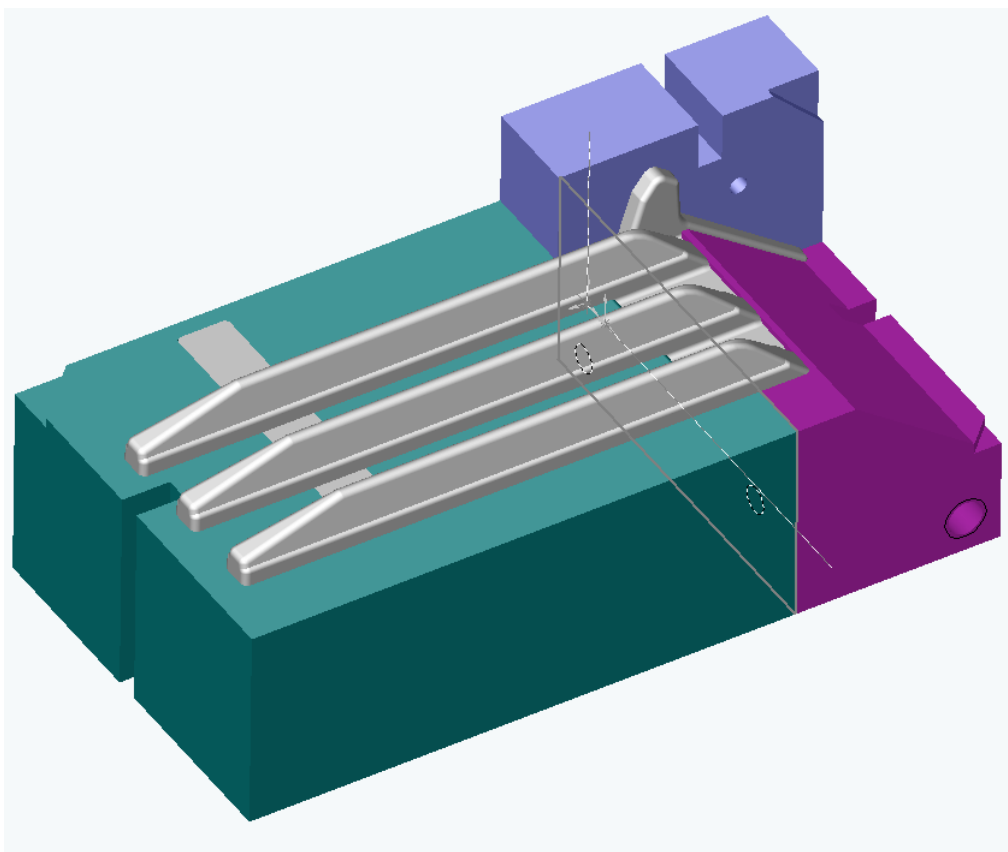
Нижняя полуматрица, вкладная часть и отливка
